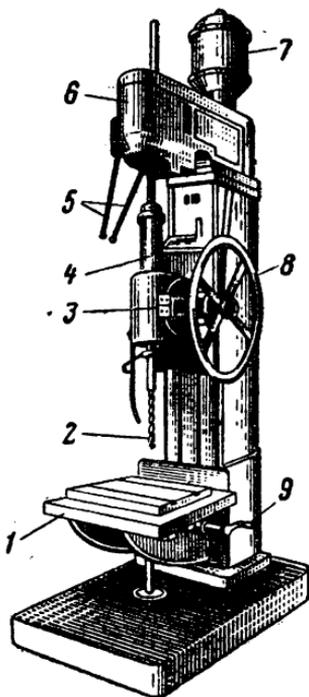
Одношпиндельный вертикально-сверлильный станок:
